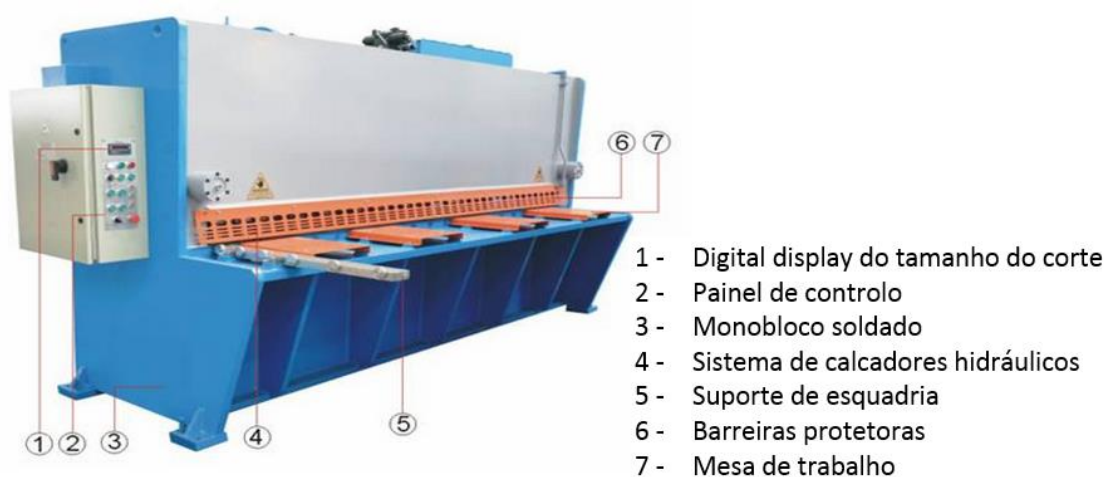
Principais componentes de uma guilhotina hidráulica – Parte frontal (Dafumt, 2014)
